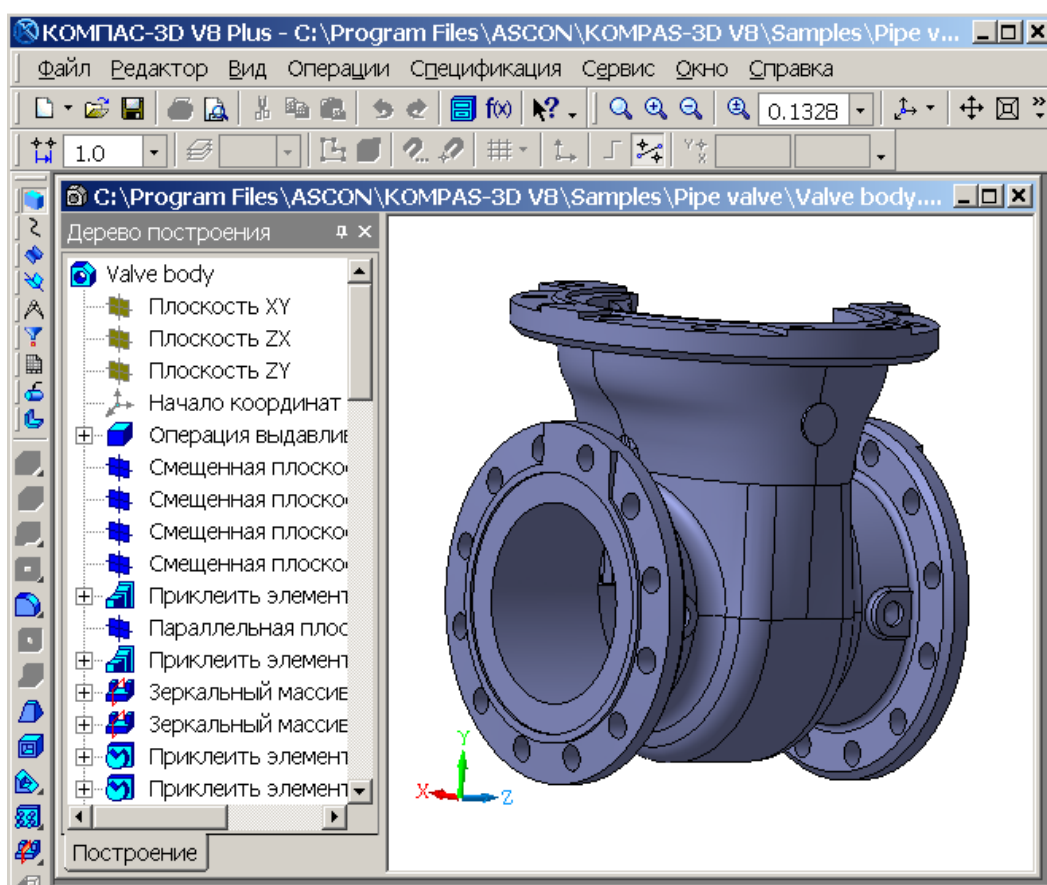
Деталь Valve body.m3d в КОМПАС
